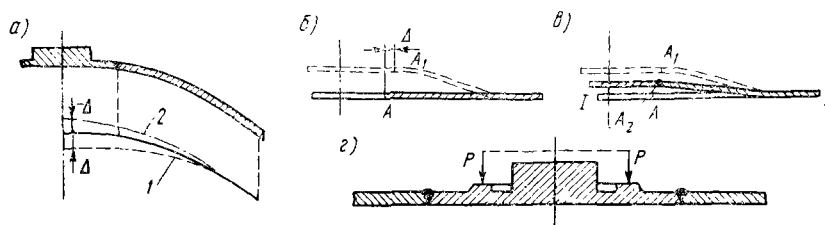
Примеры устранения перемещений, вызываемых круговыми сварными швами
